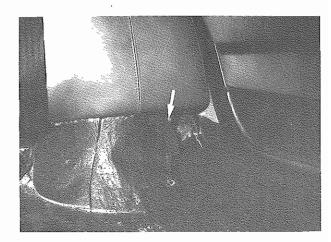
Viti fissaggio inferiore Lower fixing screws
